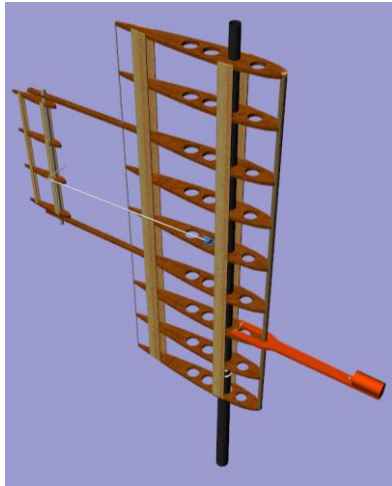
Vista en perspectiva de l'estructura de reforç de l'aparell. Font: pròpia.
